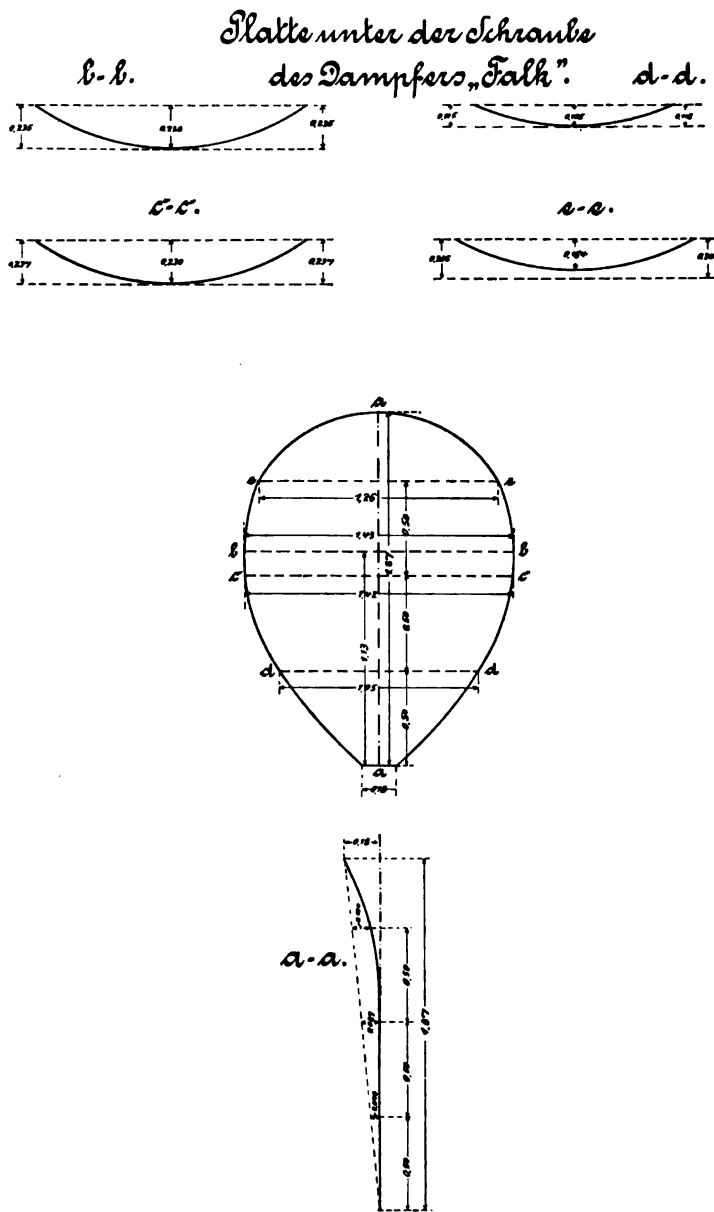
Platte unter der Schraube des Dampfers »Falk«.
